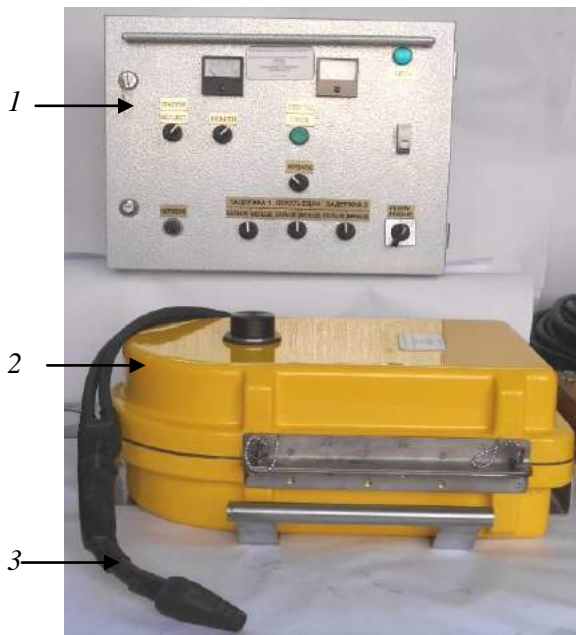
Полуавтомат для подводно сварки и резки: 1 – блок компьютеризованного управления и регулирования; 2 – погружной блок; 3 – специализированный шланговый держатель
